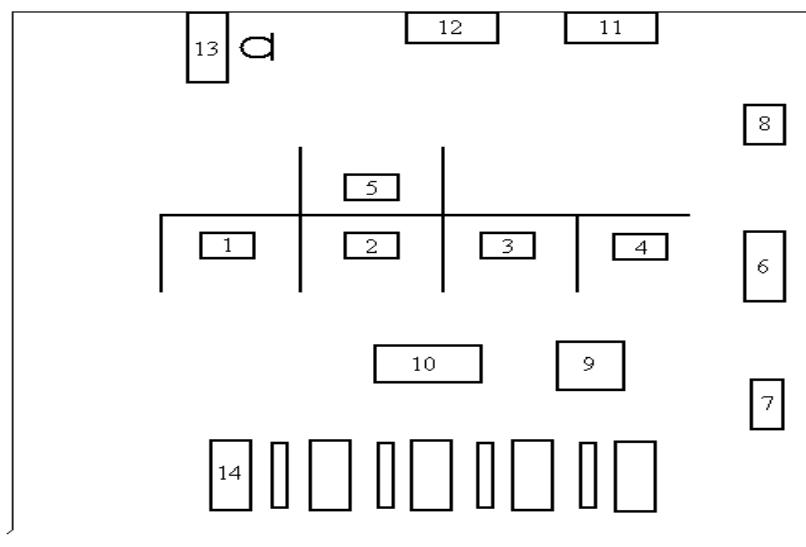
План-схема ділянки зварювання: 1-5 – місця для електродугового зварювання; 6 – місце автоматичного зварювання; 7 – місце контактного зварювання; 8 – свердлильний верстат; 9 – фрезерний верстат; 10 – заточувальний верстат; 11 – шліфувальний верстат; 12 – шафа з інструментами; 13 – робоче місце з ПК; 14 – письмові столи (5 шт.).
